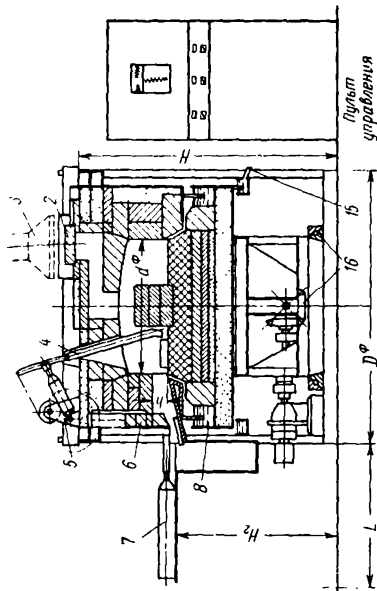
Кузнечная печь с вращающимся полом: 1 — жароупорное несущее кольцо; 2 — шибер на отходящих газах; 3 — зонт для отвода газа; 4 — балка для выдачи заготовок (охлаждается водой); 5 — пневматический цилиндр для выдачи заготовок; 6 — крышка; 7 — пневматический цилиндр для загрузки заготовок; 8 — водяной затвор; 9 — ролик; 10 — загрузочное отверстие; 11 — склиз к молоту; 12 — теплоизоляция; 13 — футеровка; 14 — форсунка для горелки; 15 — слив воды; 16 — шарнирная опора и привод, $d\phi = 1100 \div 1900$ мм, $D\phi = 2100 \div 3000$ мм; $H = 2000 \div 2100$ мм, $H_2 = 1300$ мм, $h = 200 \div 300$ мм. Производительность — 250—1250 кг/ч; расход топлива — мазут — 36—120 кг/ч
